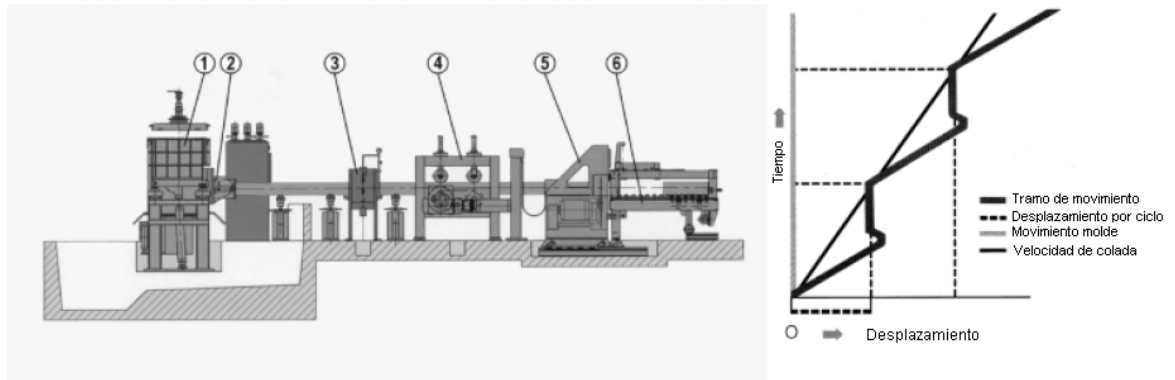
Diseño de planta y retroceso esquemático del sistema COMPUTOCAST [13]
